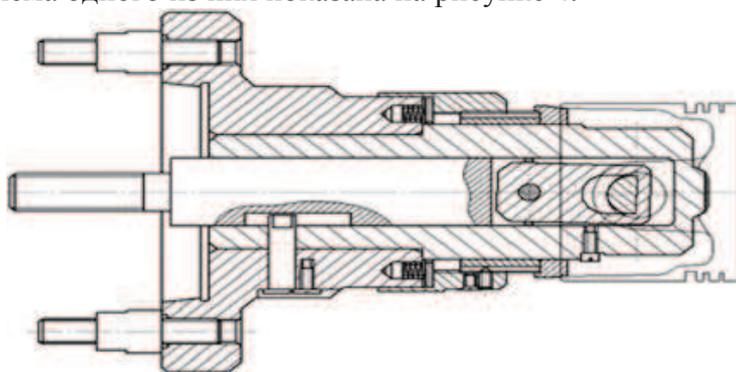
Патрон для получистовой обработки поршня и прорезки канавок под поршневые кольца
